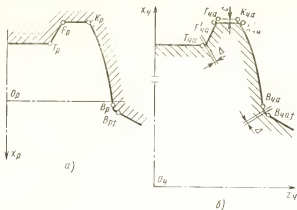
Сравнение рабочего профиля (а) инструментальной рейки и теоретического профиля (б) основного червяка червячной шлицевой фрезы
